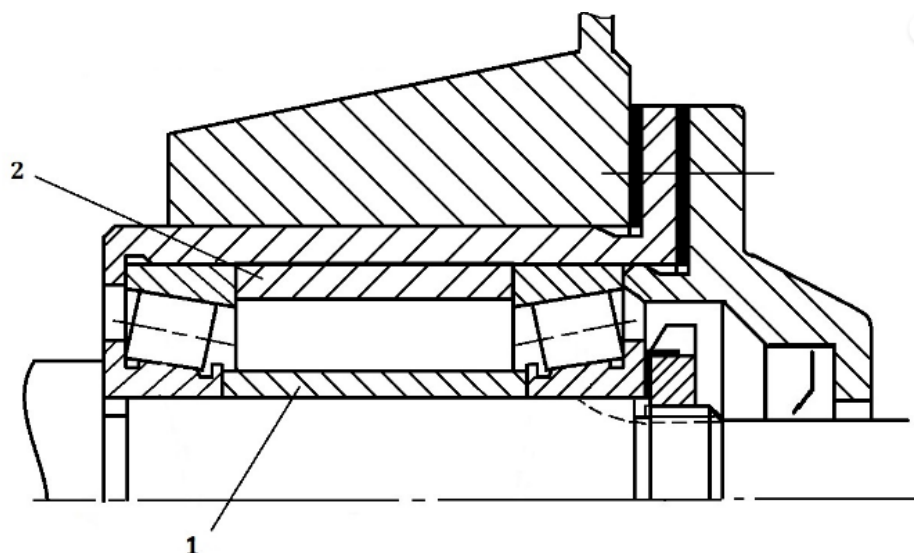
Радиально-упорные роликовые конические подшипники по схеме «врастяжку» с натягом для реверсивной работы
